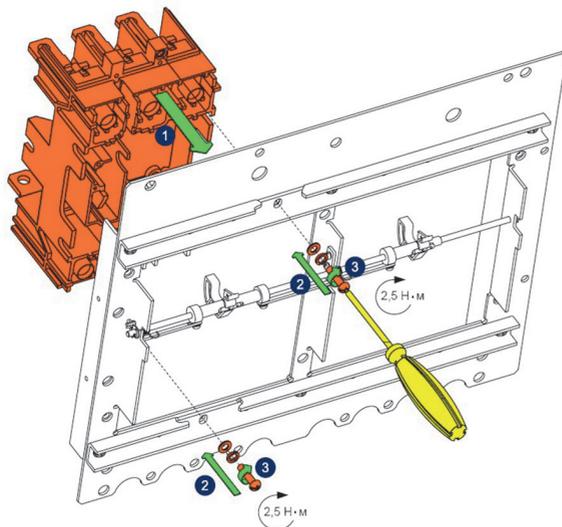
Подготовка рамы механической блокировки для установки выключателей втычного исполнения
